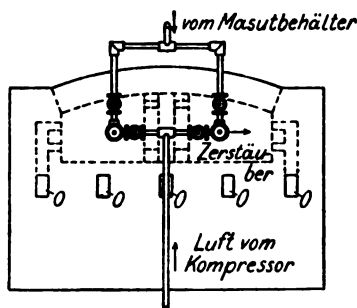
Masutfeuerung bei einem Schweißofen. Bei O wird Verbrennungsluft (Sekundärluft) in den Ofen geführt. Die Heizdüse führt das Masut in einem engen Rohr ein; außen wird dies von Druckluft umspült, die aus einem Kreisring austritt. Beides Masut und Luft werden unter Druck zugeführt (6 und 3 Atm.). Ersteres auch in einem dampfgeheizten Röhrenapparate vorgewärmt. Vgl. Heck, Masutfeuerungen, Stahl und Eisen, 1904, S. 1430.
